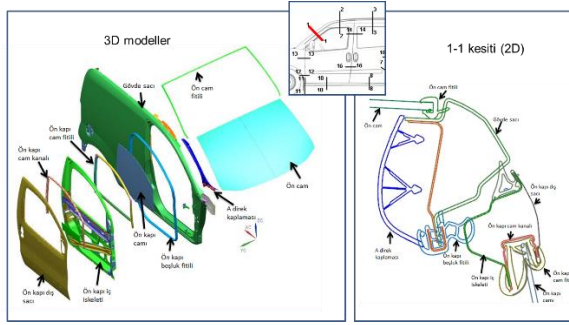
Örnek stil kabuğuna ait içi boş kesit (An example for hollow cross-section of style shell)
